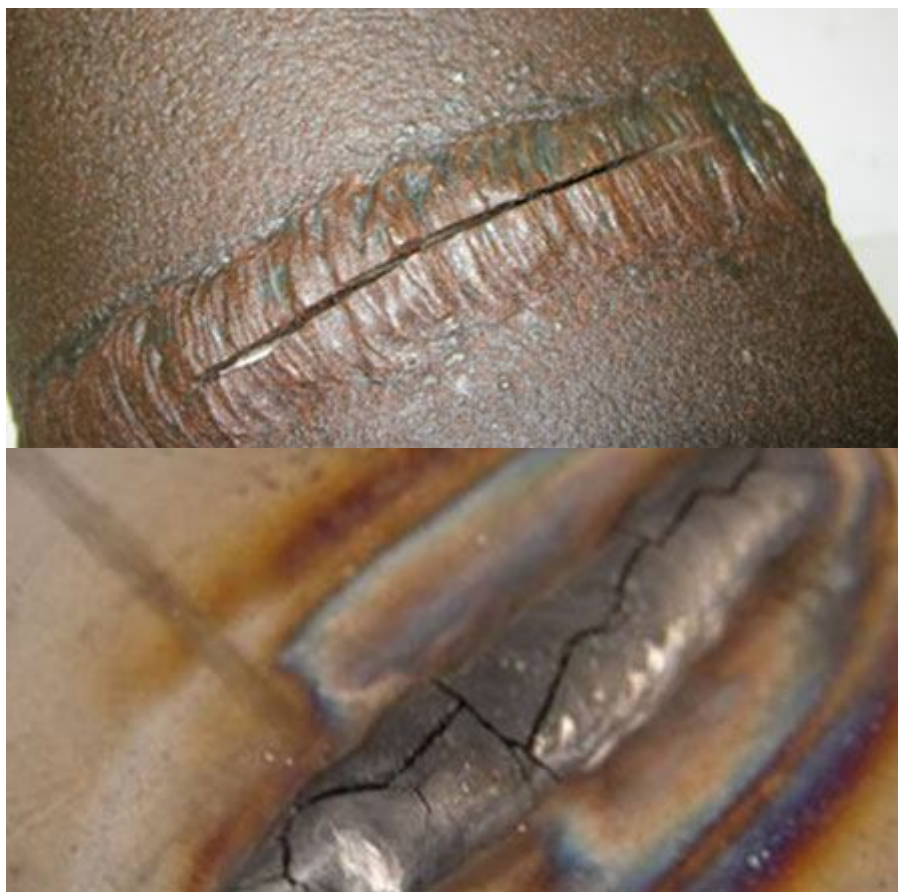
Дефекты сварного шва: трещины
